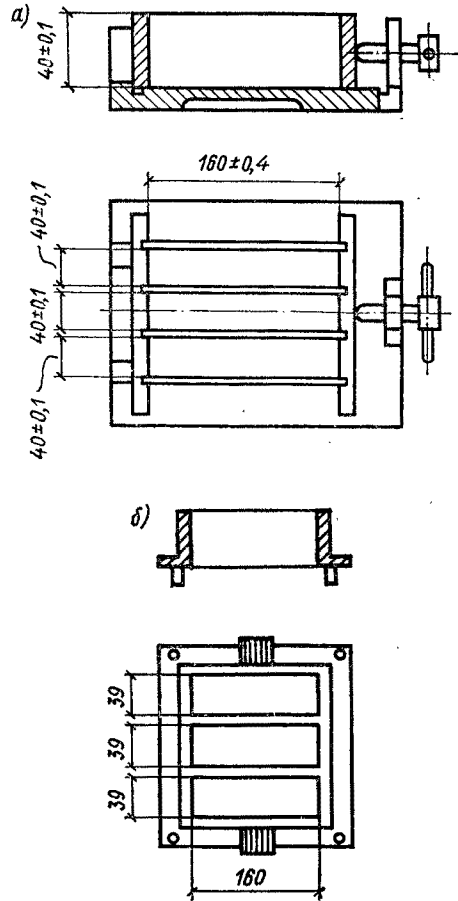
Конструкция формы (а) для приготовления цементных образцов-балочек и насадки (б) к ней
